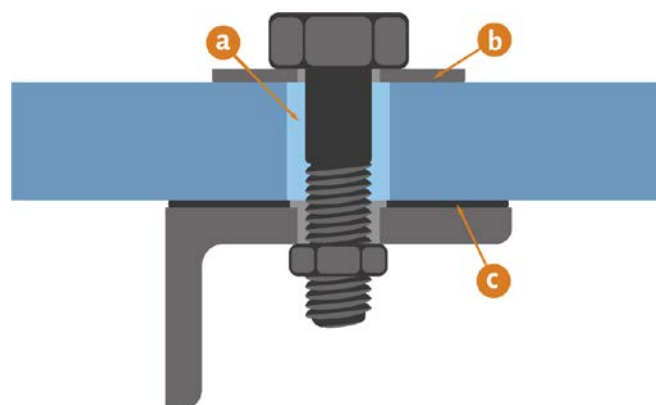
Befestigung mit sichtbarer Verschraubung
